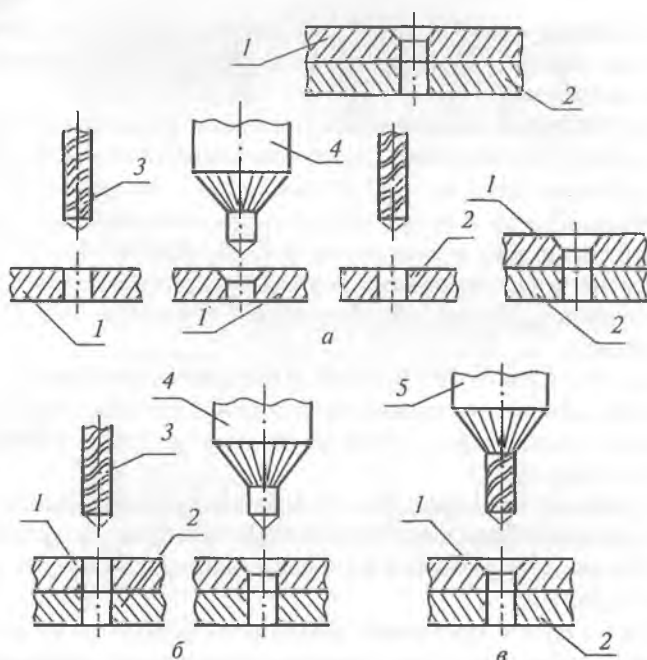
Различные варианты образования отверстий и гнезд под потайную головку заклепки: а — сверление и зенкование раздельно в каждой детали; б — сверление и зенкование в пакете с применением двух инструментов; в — сверление и зенкование в пакете одним инструментом: 1, 2 — детали пакета; 3 — сверло; 4 — зенковка; 5 — сверло-зенковка
